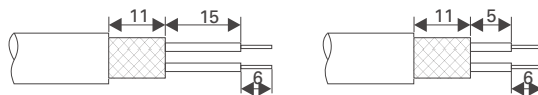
Verdrahtungsbeispiel mit Schraubadapter
